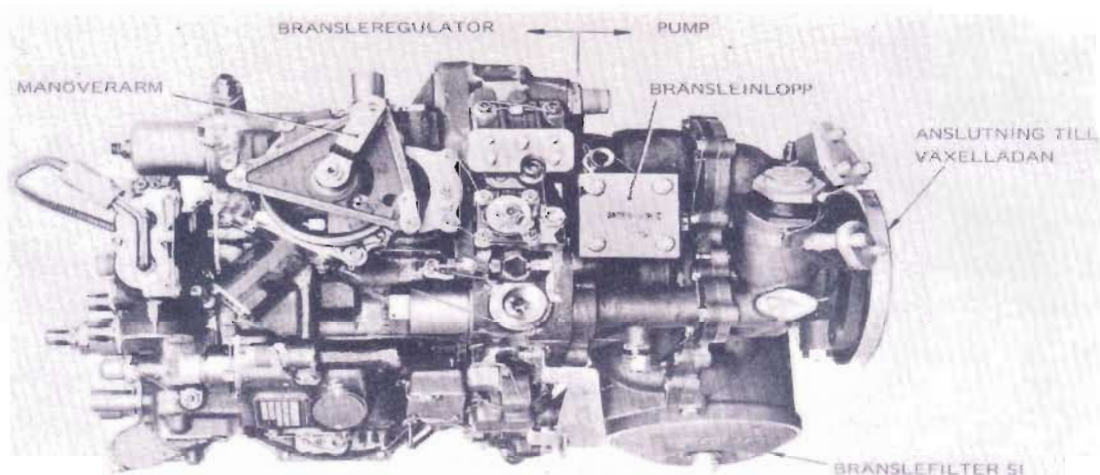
4 Gg-pumpen och bränsleregulatorn, exteriör.
